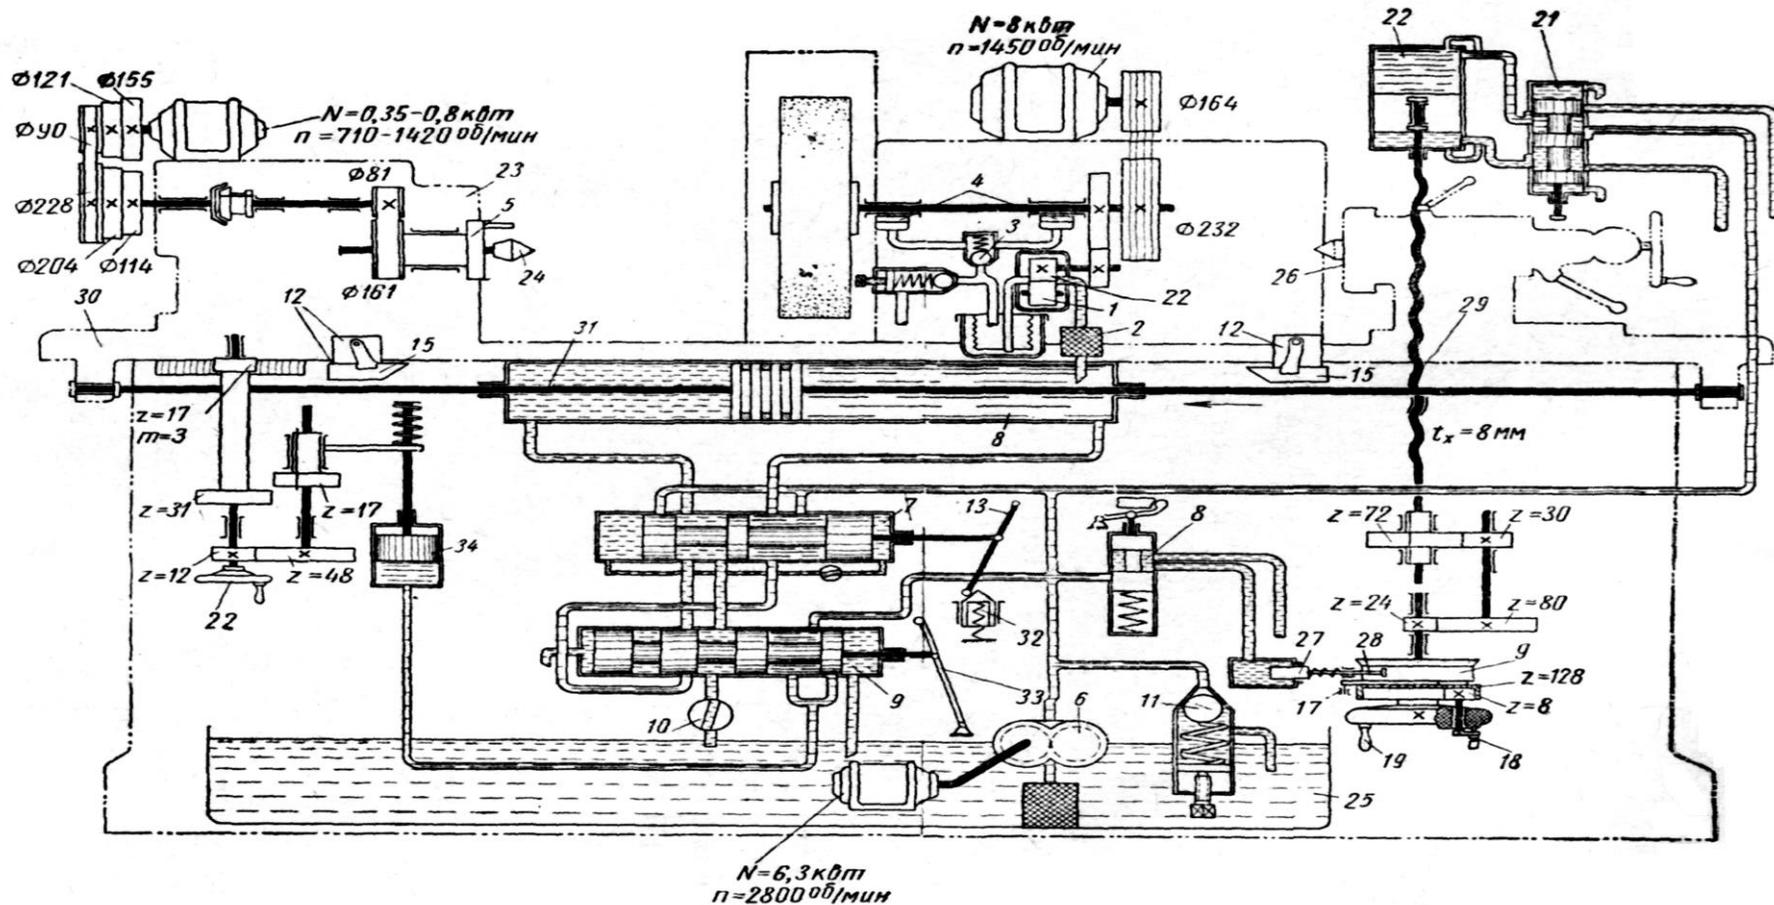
Гидрокинематическая схема круглошлифовального станка модели 3151
